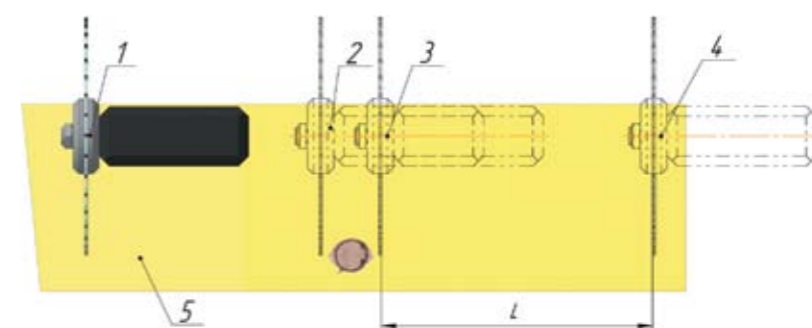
Схемы резания: положения торцовочной пилы: 1, 4 – подрезка торцов; 2 – деление заготовки; 2, 3 – выборка дефектных мест; 3, 4 – вырезка заготовки мерной длины; 5 – пиломатериал
